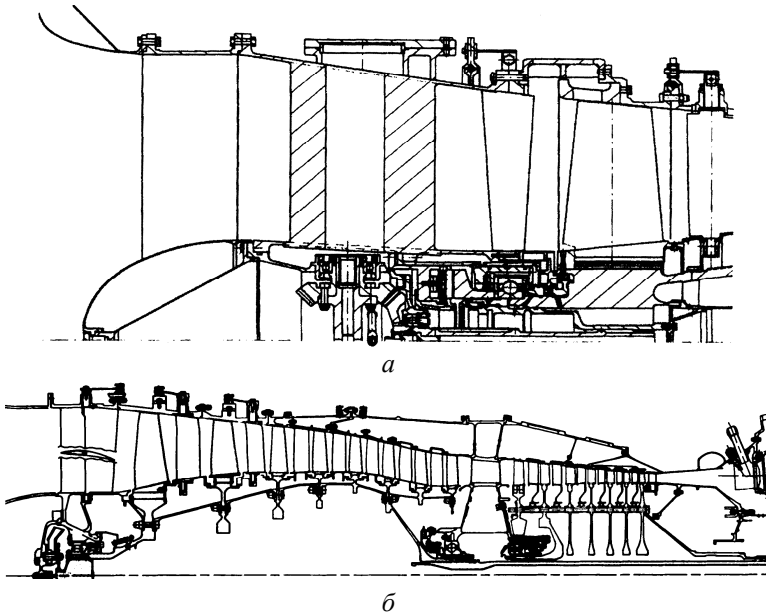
Конструкция передней опоры КНД ГТУ UGT16000 (а) и компоновка опор КНД и КВД в ГТУ FT8 (б) [9, 6].
